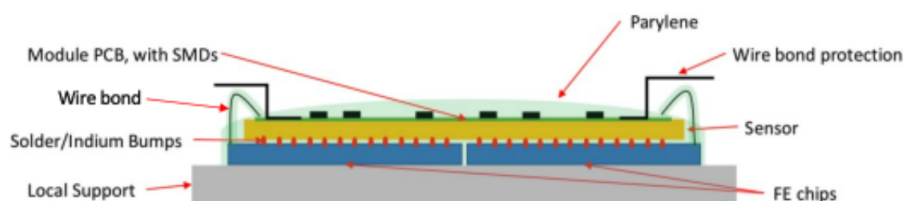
Schema del modulo assemblato dagli enti di ricerca
